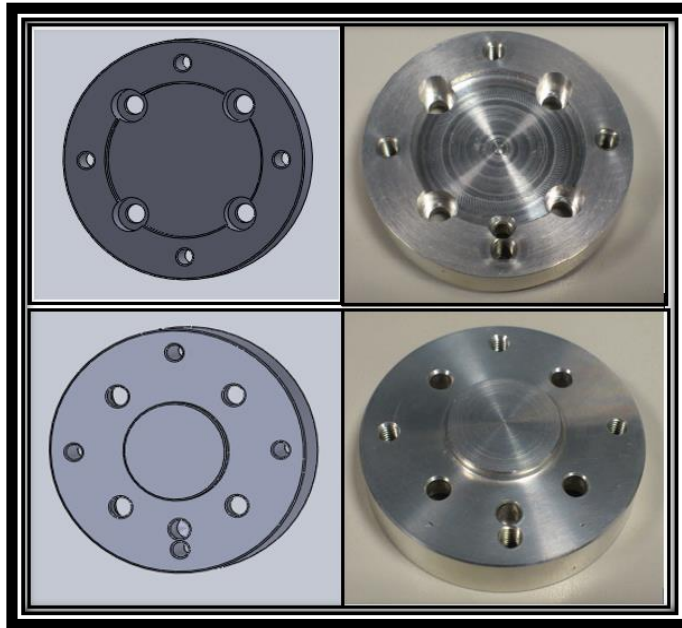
Projeto da flange para a garra da Bosch em SolidWorks (à esquerda) e flange para a garra da Bosch (direita)
